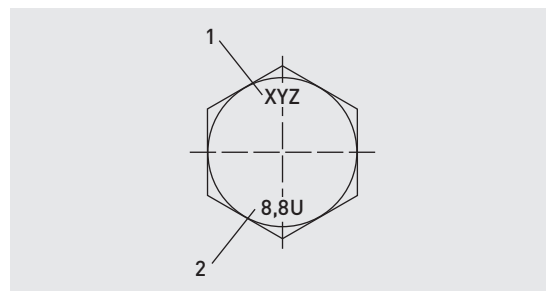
Beispiel der Kennzeichnung feuerverzinkter Gewidemuttern und -schrauben vor Aufbringen des Überzugs mit Gewindeuntermass gemäss Toleranz 6az
